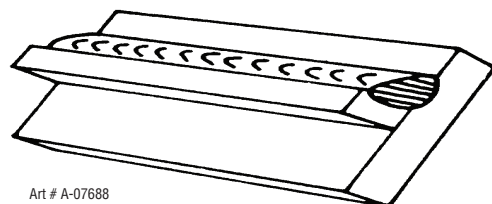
Posición plana, soldadura de ángulo en gravedad
